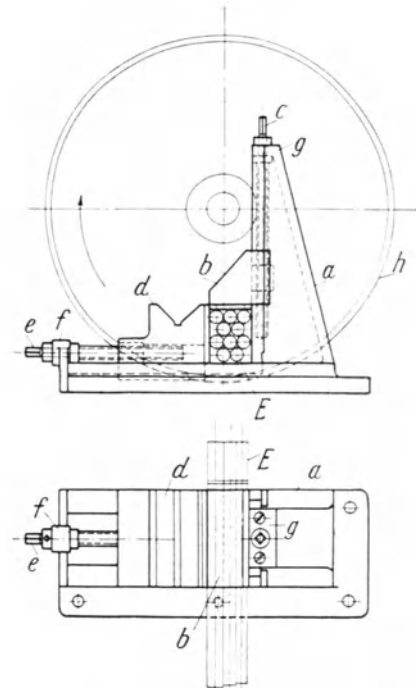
Universal-Spannvorrichtung für Kaltsägen.
